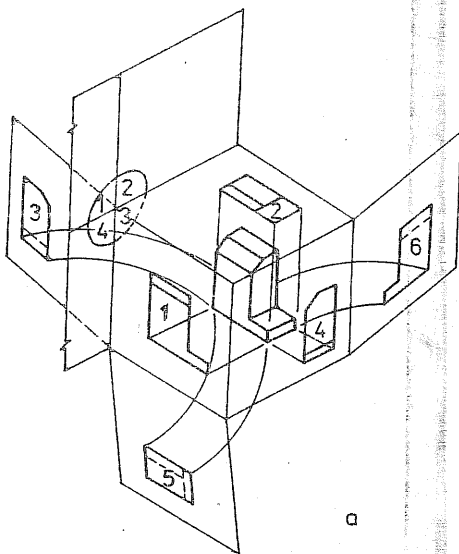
Základná metóda zobrazovania premietaním v 1. kvadrante, metóda E
